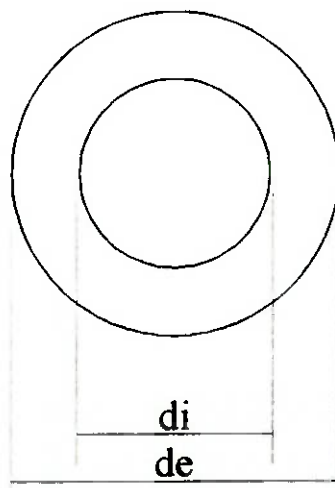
Dimensões do corpo de prova do ensaio rotativo.
